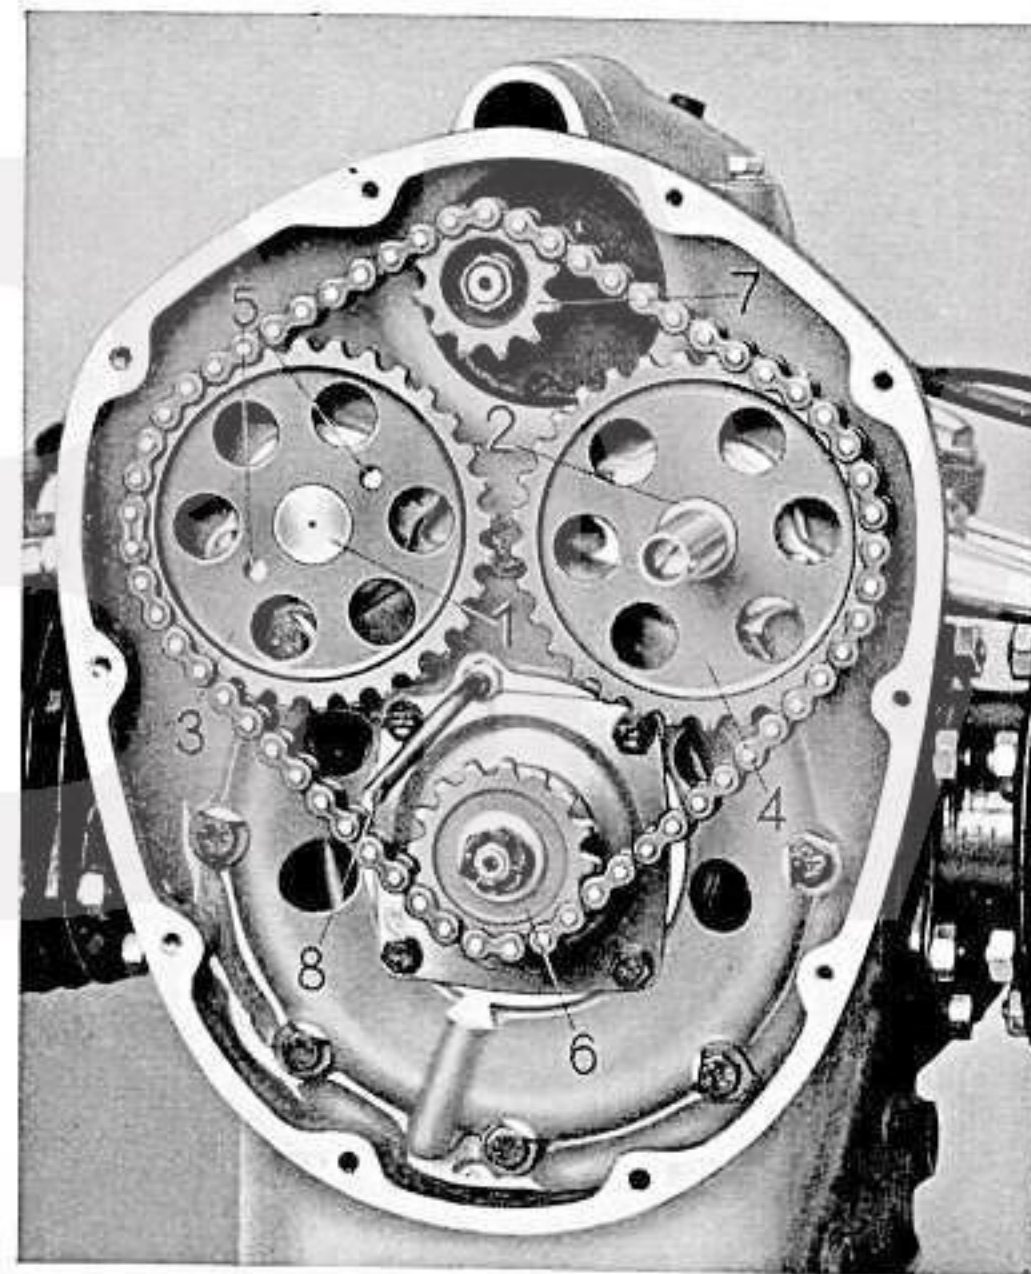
Nockenwellen und Lichtmaschinenantrieb der R 5-Maschine
